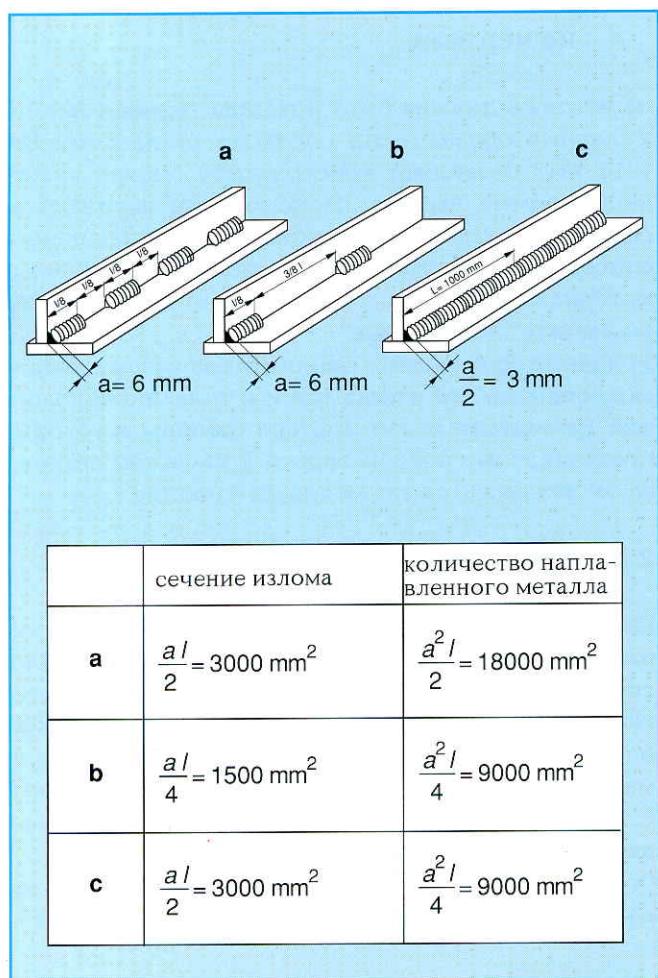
Сравнение угловых швов, полученных сваркой прерывистым швом и сваркой напроход
